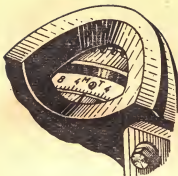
Установка коленчатого вала автомобиля ГАЗ-51 (в положении поршня первого цилиндра в в. м. т.).
